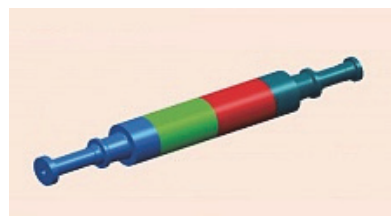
Прототип сварного ротора для турбогенератора 900 МВт
